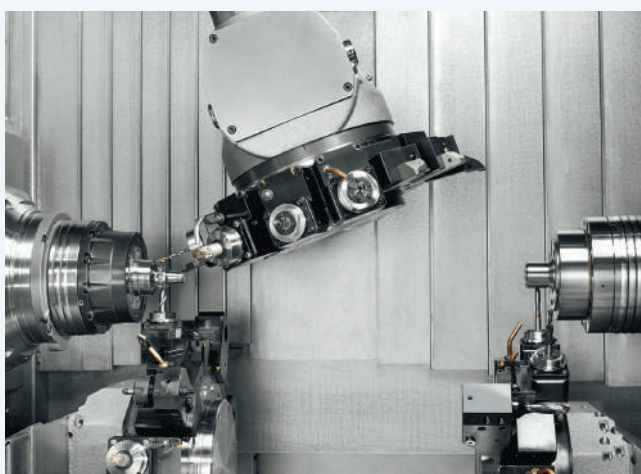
Токарно-фрезерный станок с тремя револьверными головками, одна из которых оснащена поворотной В-осью
